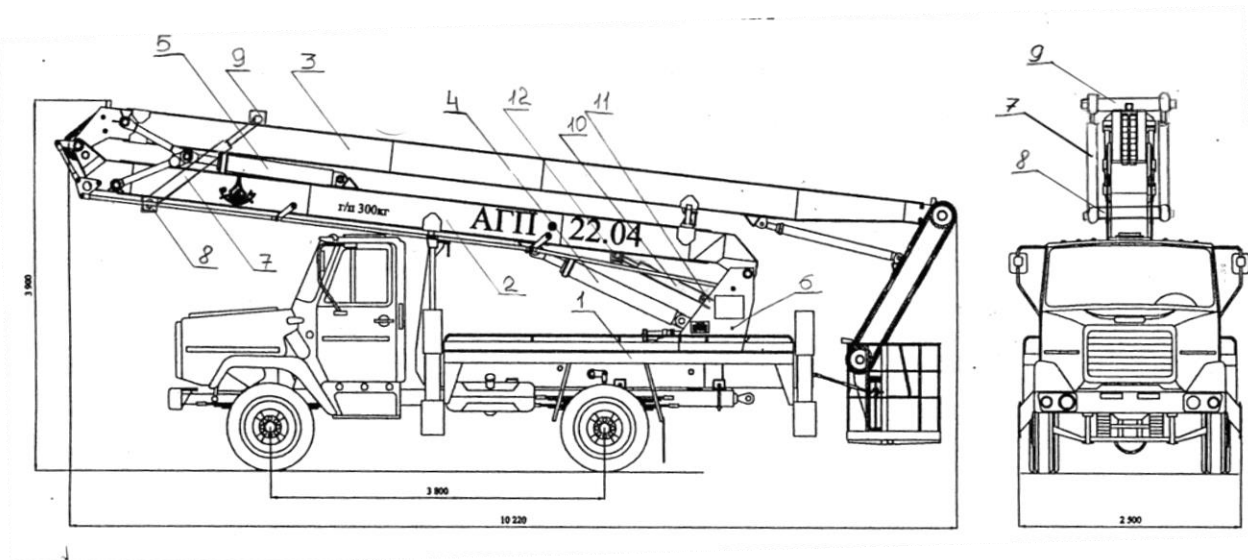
Расположение разрабатываемого устройства на схеме автовышки в транспортном положении: 1 – автовышка; 2 – нижнее колено автовышки; 3 – верхнее колено; 4 – рабочий гидроцилиндр подъема нижнего колена; 5 – рабочий гидроцилиндр подъема нижнего колена; 6 – опорно-поворотное устройство автовышки; 7 – предохранительное устройство для второго колена; 8, 9 – кронштейны предохранительного устройства для второго колена; 10 – предохранительное устройство для нижнего колена; 11 – фланец крепления опорной части предохранительного устройства для нижнего колена; 12 – кронштейн крепления верхней части предохранительного устройства для нижнего колена
